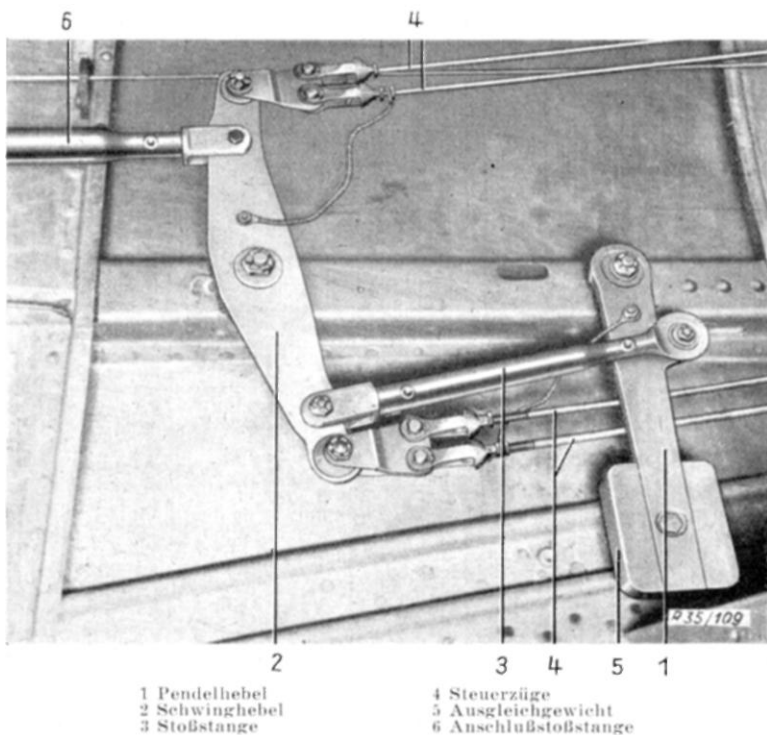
Pendelhebel und Schwinghebel mit Ausgleichgewicht für Höhensteuerung
